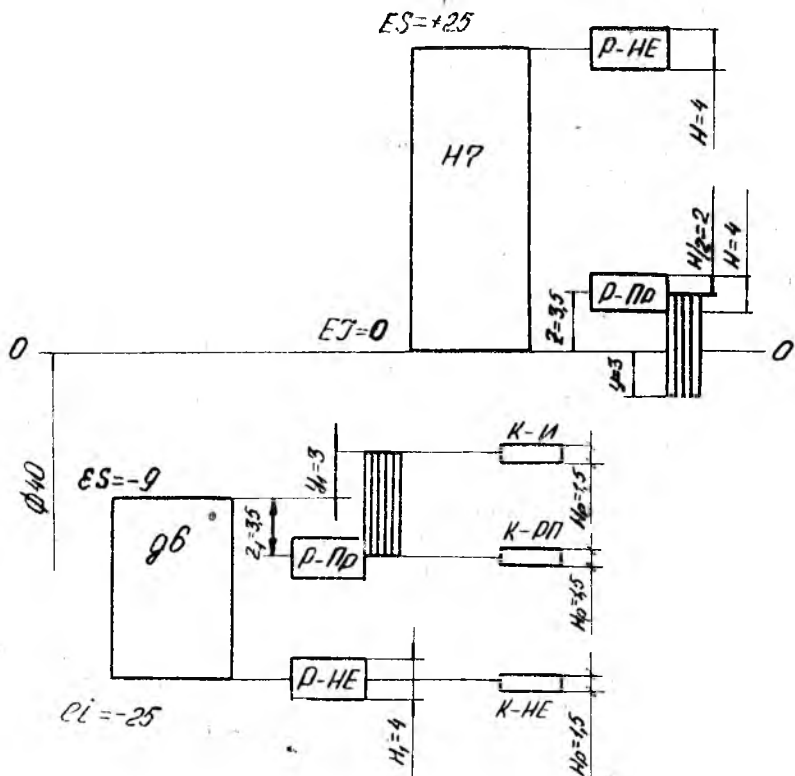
Схема расположения полей допусков калибров для контроля деталей сопряжения  $\phi 40$  H7 — g 6
